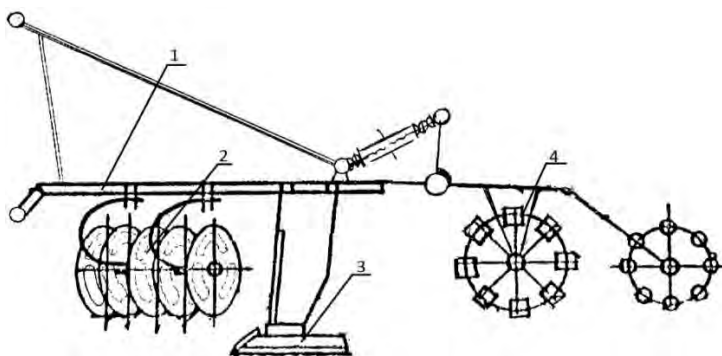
Конструктивная схема агрегата для послойной обработки почвенного пласта:
